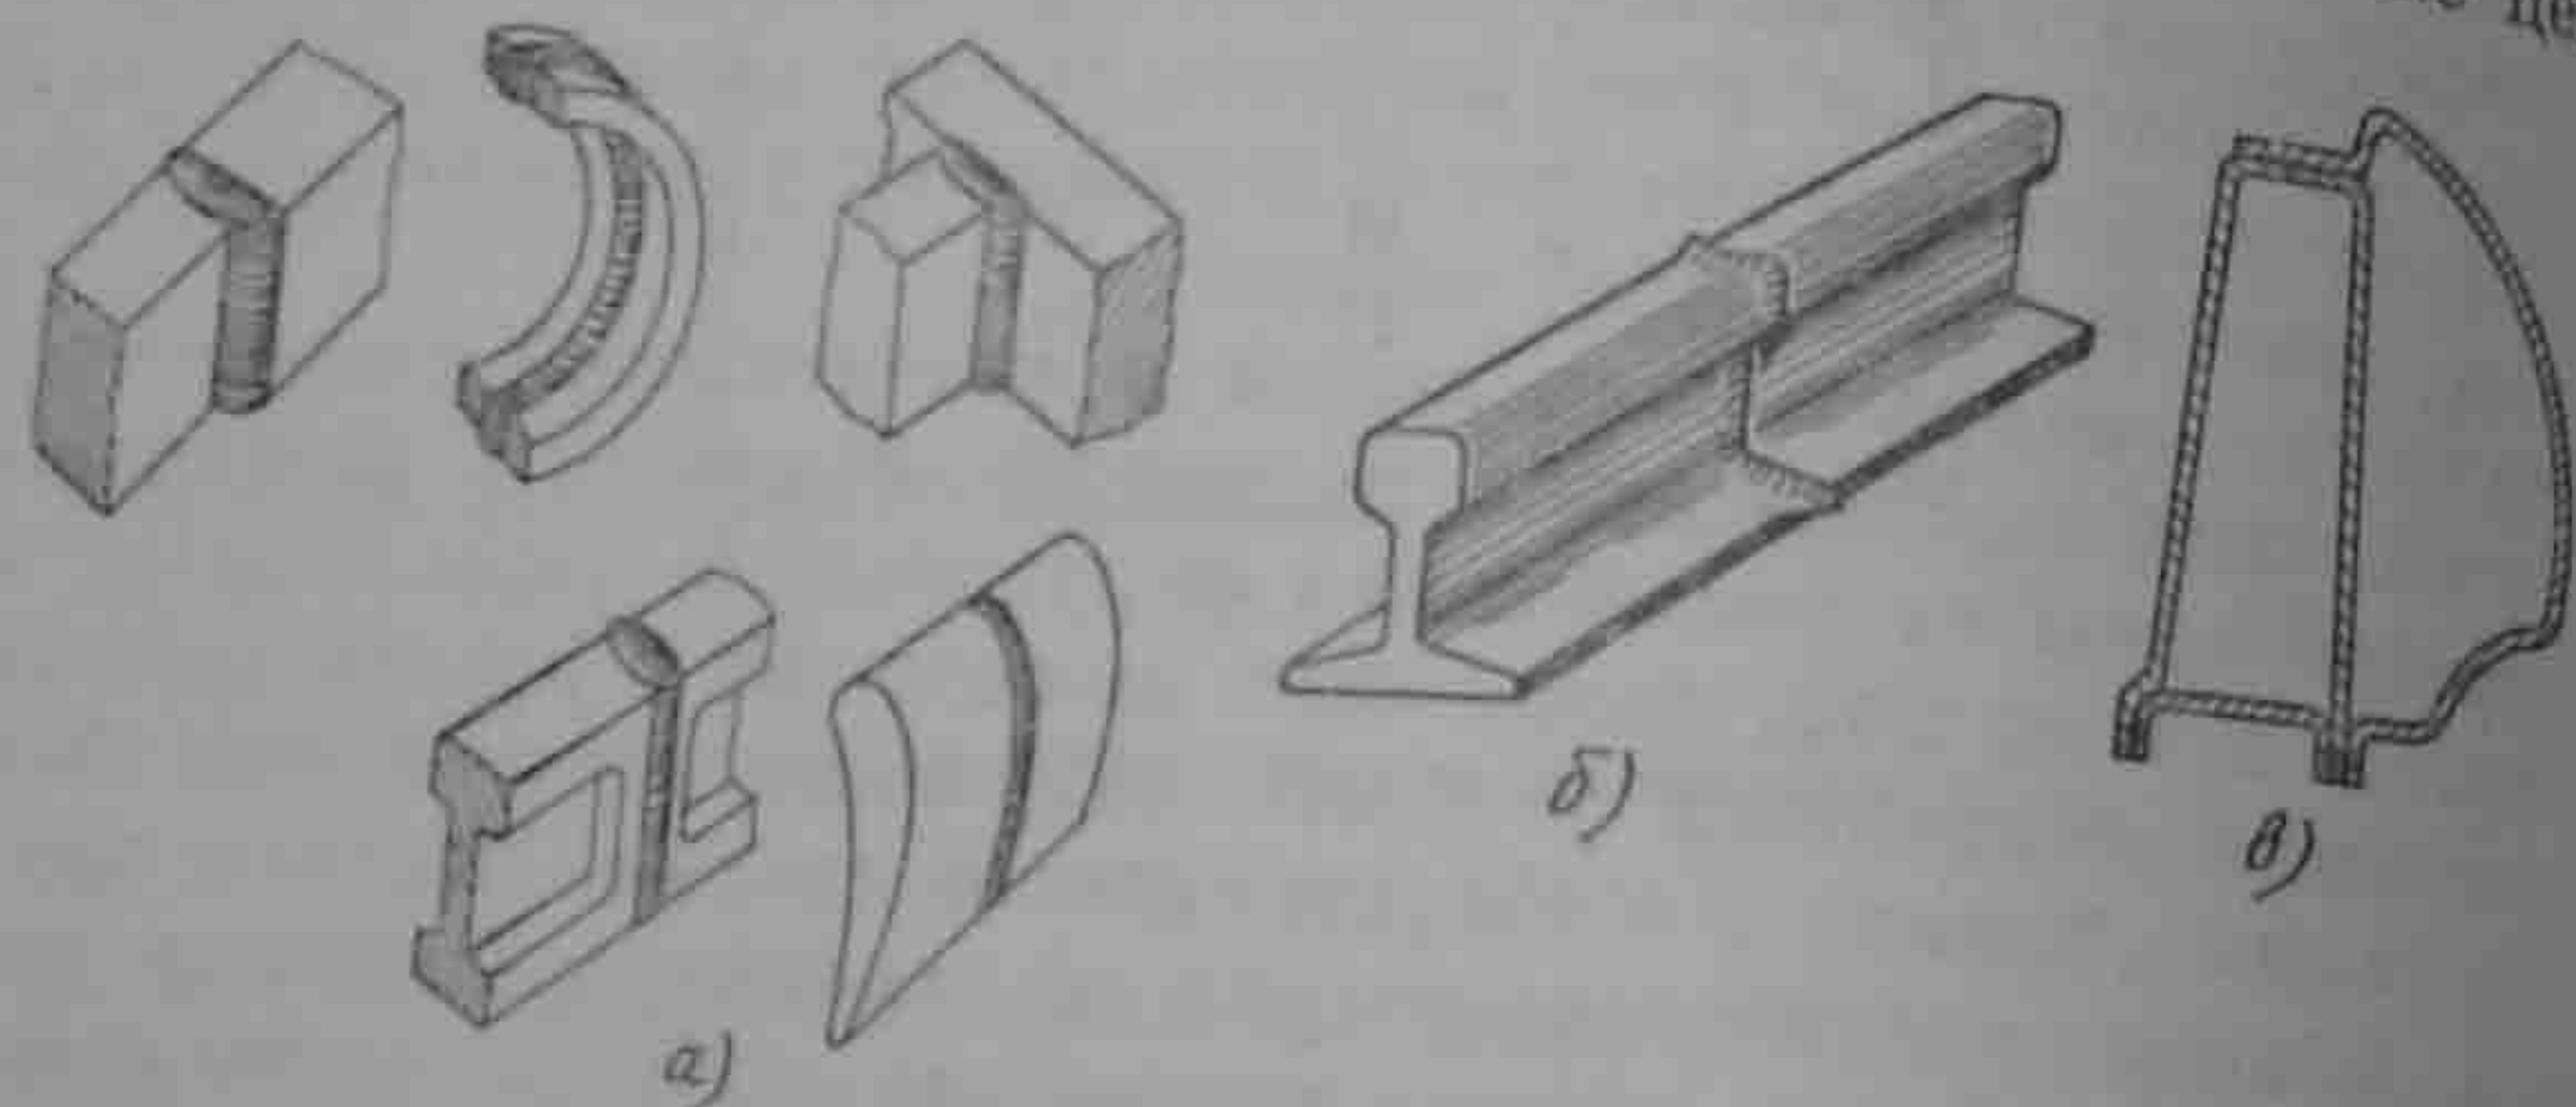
Примеры применения электрошлаковой сварки крупногабаритных заготовок (а), контактной стыковой сварки рельс (б) и контактной точечной сварки ветровой рамы автомобиля (в)
